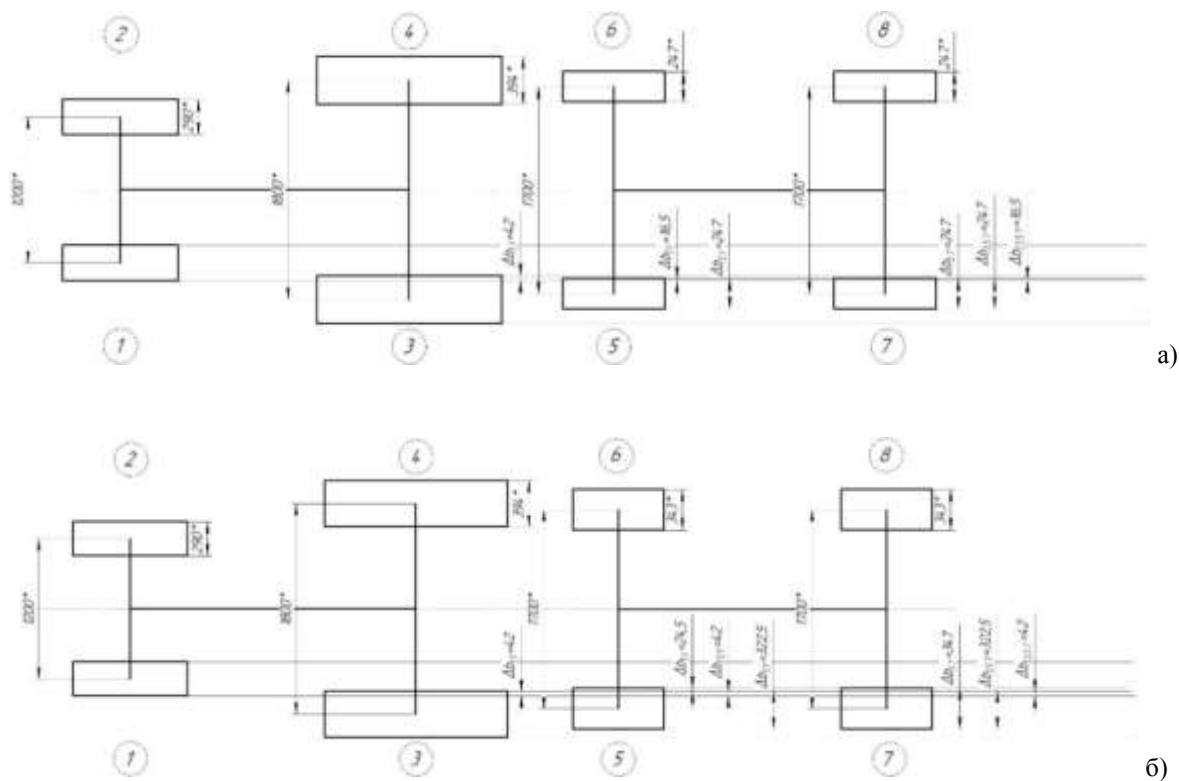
Определение перекрытия следов МТЗ-82+2ПТС-4М:
